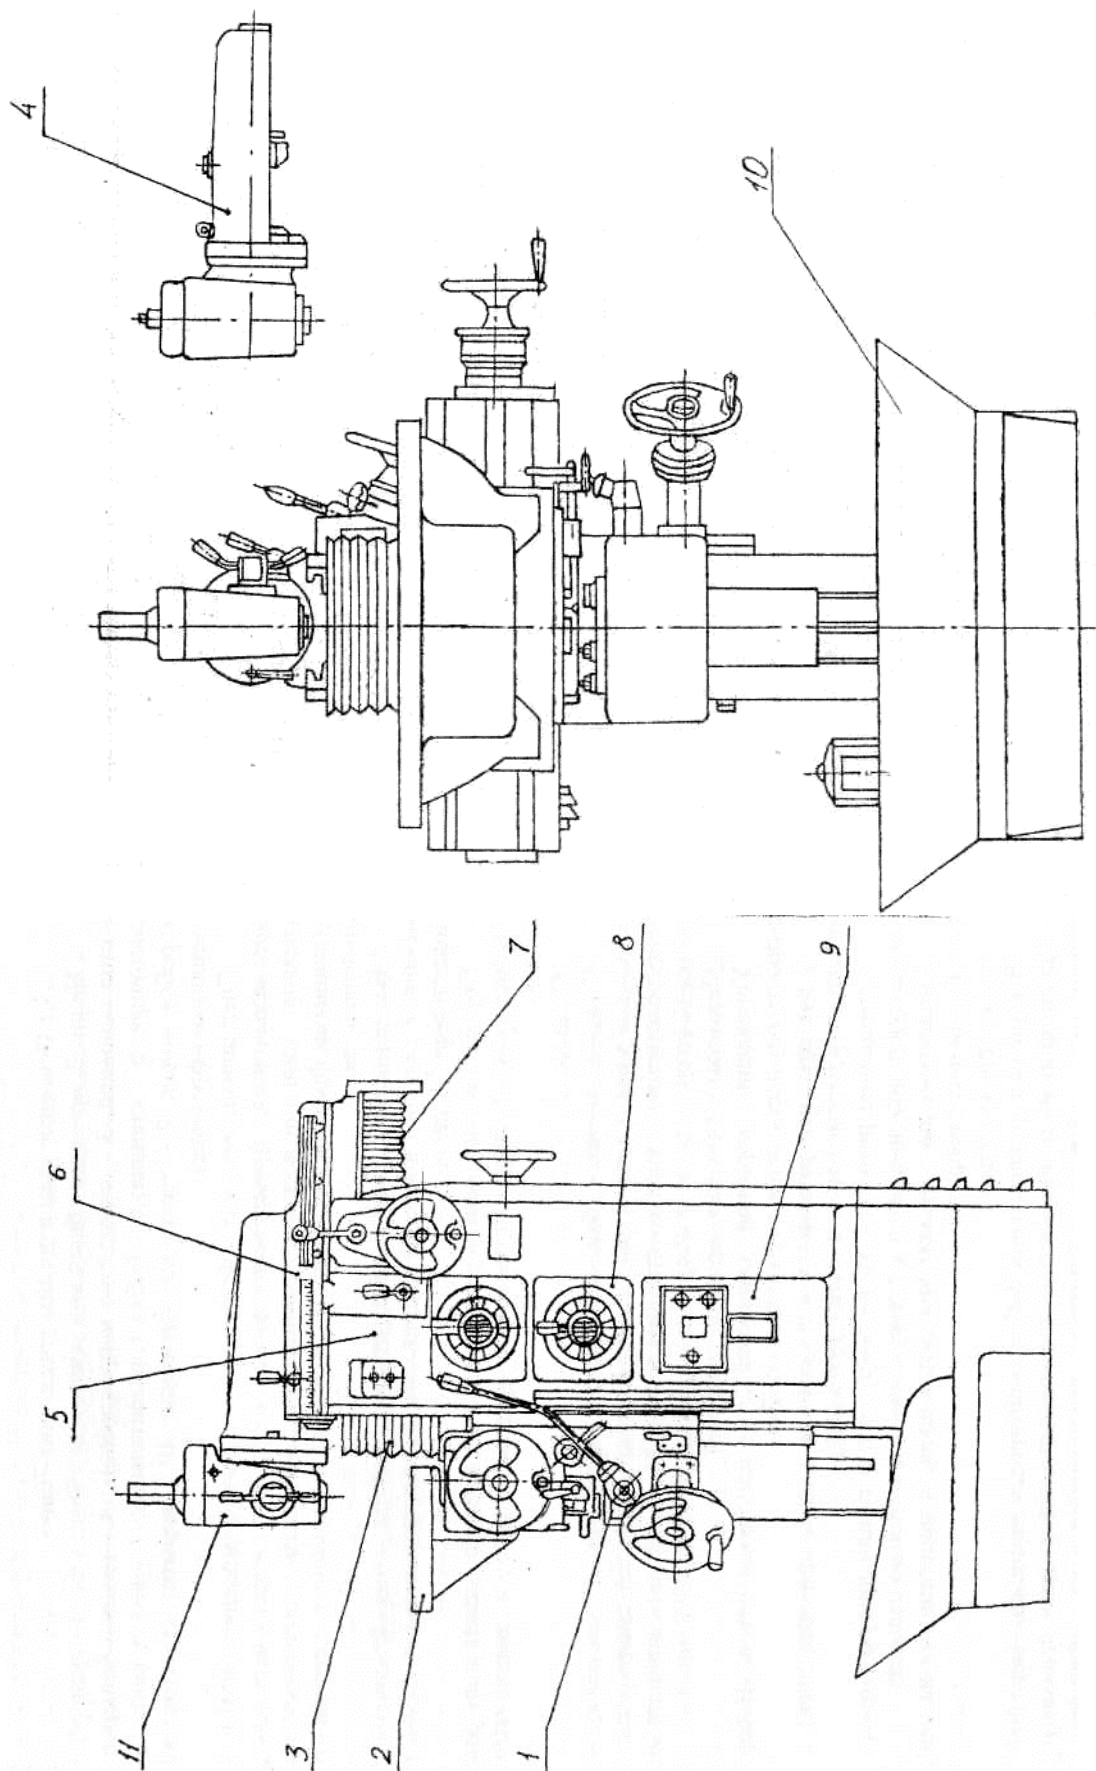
Общий вид специализированного фрезерного станка мод. ВМ 130Н
